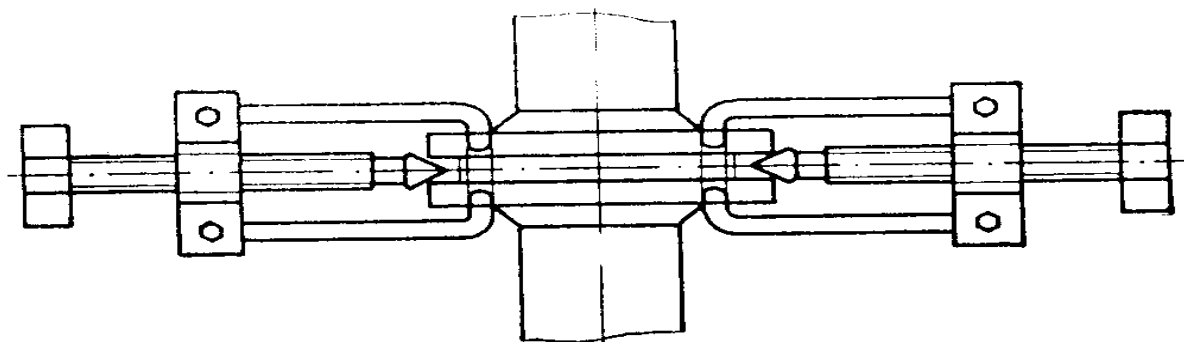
Винтовое приспособление для раздвижки фланцев
